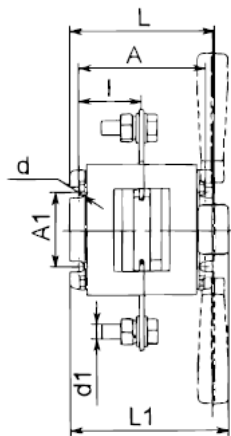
Выключатель-разъединитель однополюсный на два направления с боковой ручкой.
